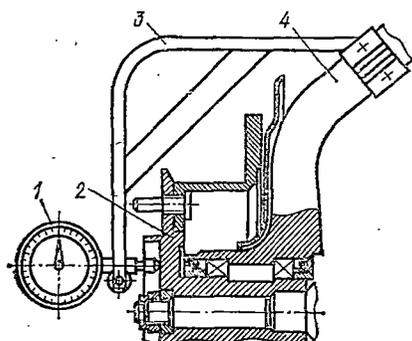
Приспособление 67.7834-9507 для измерения зазоров в подшипниках ступицы переднего колеса автомобиля ВАЗ-2121:
